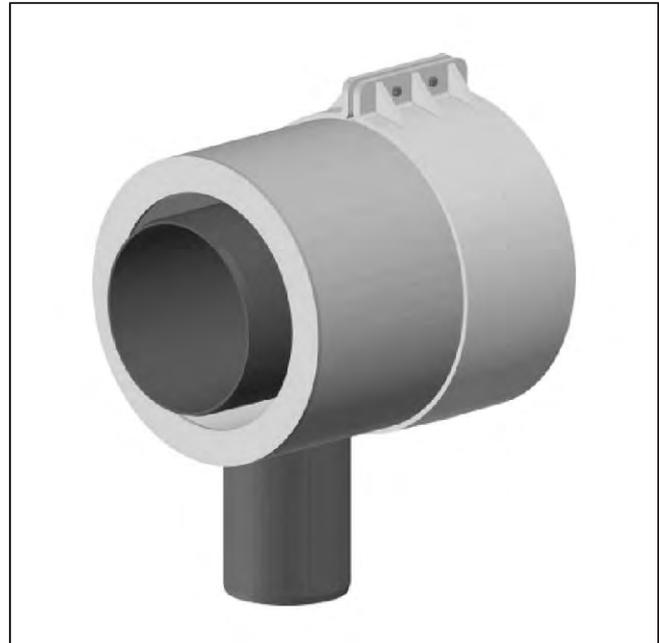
Anschluss DN80/125 für RLU Betrieb mit Zuluftstutzen
